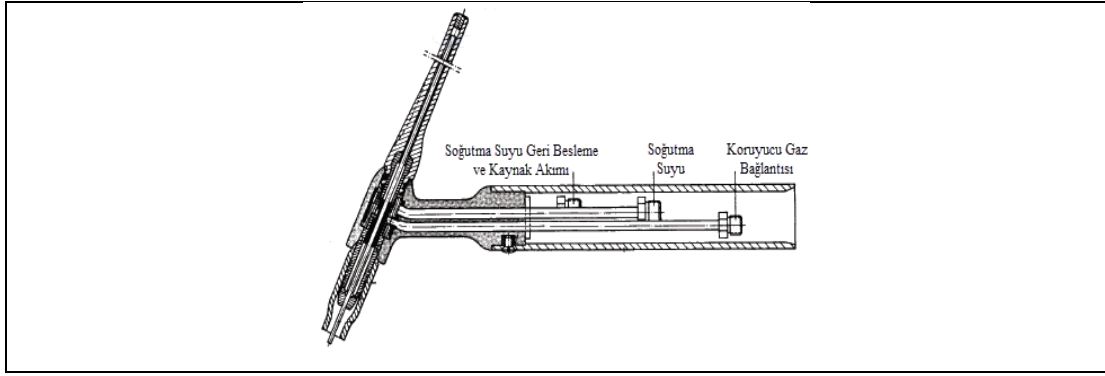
Kaynak işlemi ve kaynak torcu tutucusu [27]
